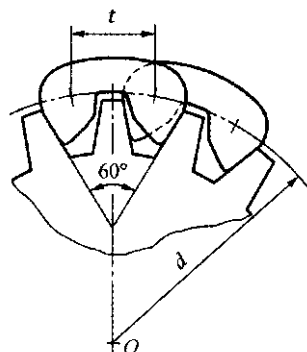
Шарнир скольжения зубчатой цепи
